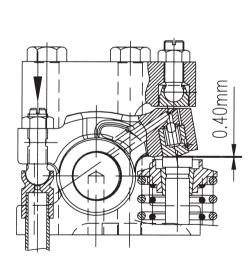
冷态排气门总气门间隙0.4mm Fig. 2 Total Valve Clearance of Cold-State Exhaust Valve 0.4mm
